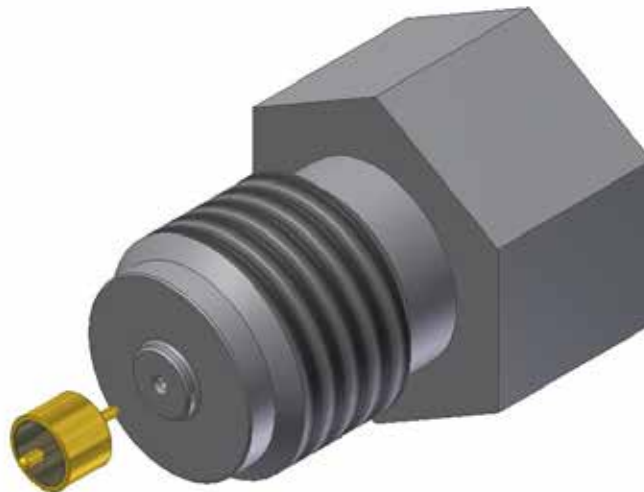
Приспособление для пайки гермоввода для устройств, использующих блочный резьбовой корпус КМПП (ЖНКЮ.713723.003)
